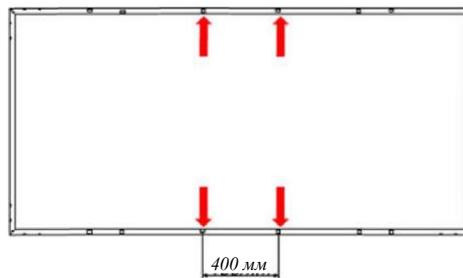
Установка с монтажными отверстиями с шагом 400 мм и болтами для одноосного поворотного устройства
